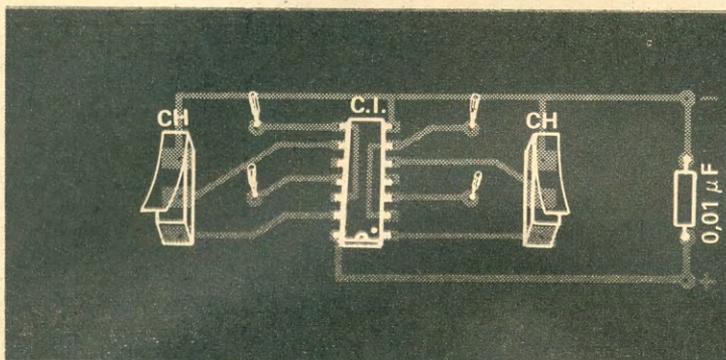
Disposição dos componentes sobre a plaqueta de circuito impresso.
